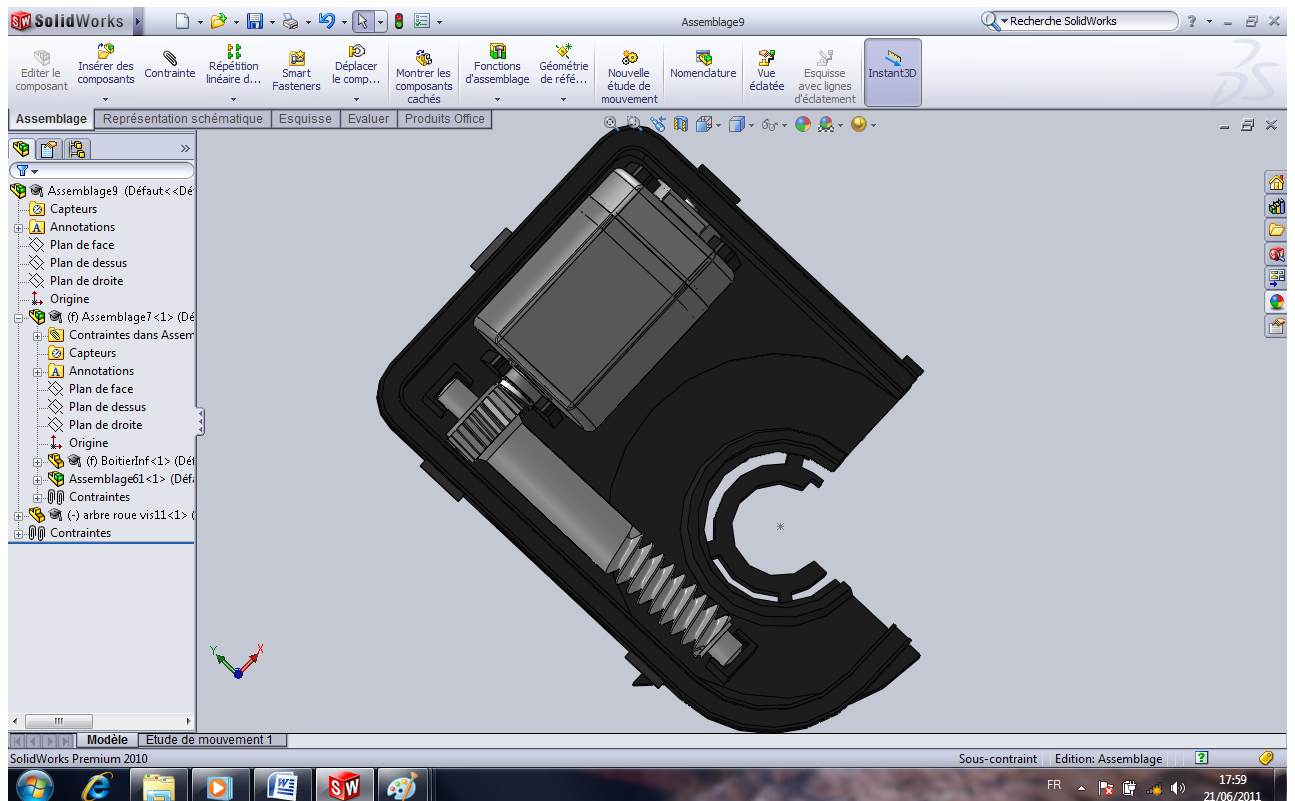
Assemblage 8(assemblage 7+arbre roue vis)
